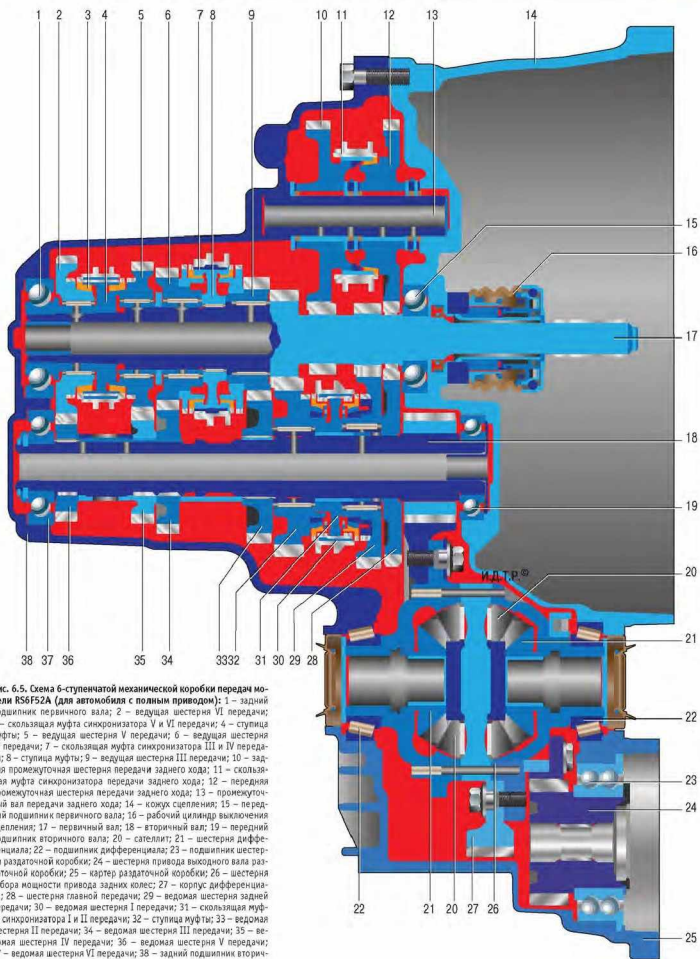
Схема 6-ступенчатой механической коробки передач модели RS6F52A (для автомобиля с полным приводом): 1 – задний подшипник первичного вала; 2 – ведущая шестерня VI передачи; 3 – скользящая муфта синхронизатора V и VI передачи; 4 – ступица муфты; 5 – ведущая шестерня V передачи; 6 – ведущая шестерня IV передачи; 7 – скользящая муфта синхронизатора III и IV передачи; 8 – ступица муфты; 9 – ведущая шестерня III передачи; 10 – задняя промежуточная шестерня передачи заднего хода; 11 – скользящая муфта синхронизатора передачи заднего хода; 12 – передняя промежуточная шестерня передачи заднего хода; 13 – промежуточный вал передачи заднего хода; 14 – кожух сцепления; 15 – передний подшипник первичного вала; 16 – рабочий цилиндр выключения сцепления; 17 – первичный вал; 18 – вторичный вал; 19 – передний подшипник вторичного вала; 20 – сателлит; 21 – шестерня дифференциала; 22 – подшипник дифференциала; 23 – подшипник шестерни раздаточной коробки; 24 – шестерня привода выходного вала раздаточной коробки; 25 – картер раздаточной коробки; 26 – шестерня отбора мощности привода задних колес; 27 – корпус дифференциала; 28 – шестерня главной передачи; 29 – ведомая шестерня задней передачи; 30 – ведомая шестерня I передачи; 31 – скользящая муфта синхронизатора I и II передачи; 32 – ступица муфты; 33 – ведомая шестерня II передачи; 34 – ведомая шестерня III передачи; 35 – ведомая шестерня IV передачи; 36 – ведомая шестерня V передачи; 37 – ведомая шестерня VI передачи; 38 – задний подшипник вторичного вала; 39 – картер коробки передач
